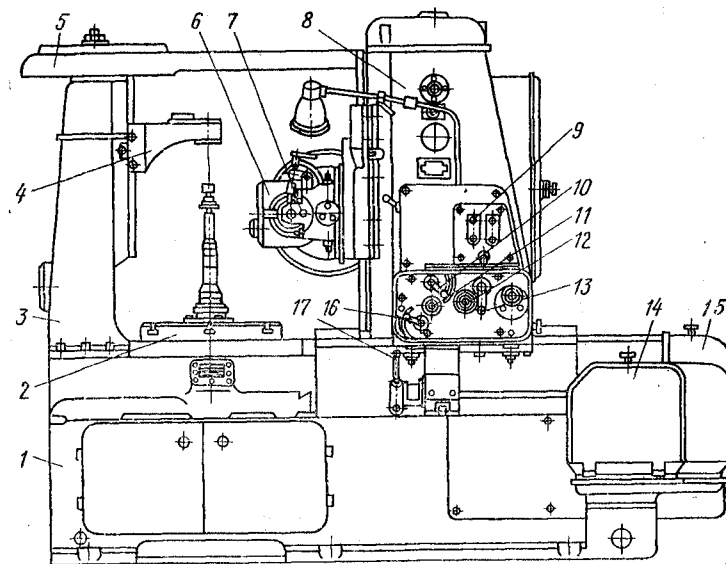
Зубофрезерный полуавтомат модели 5Д32
